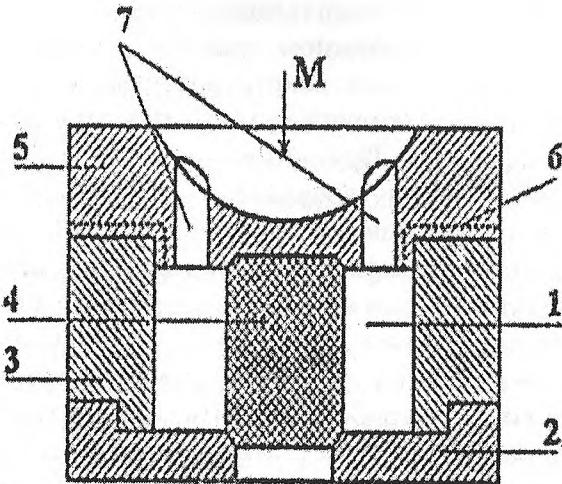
Эскиз разреза металлической формы – кокиля
